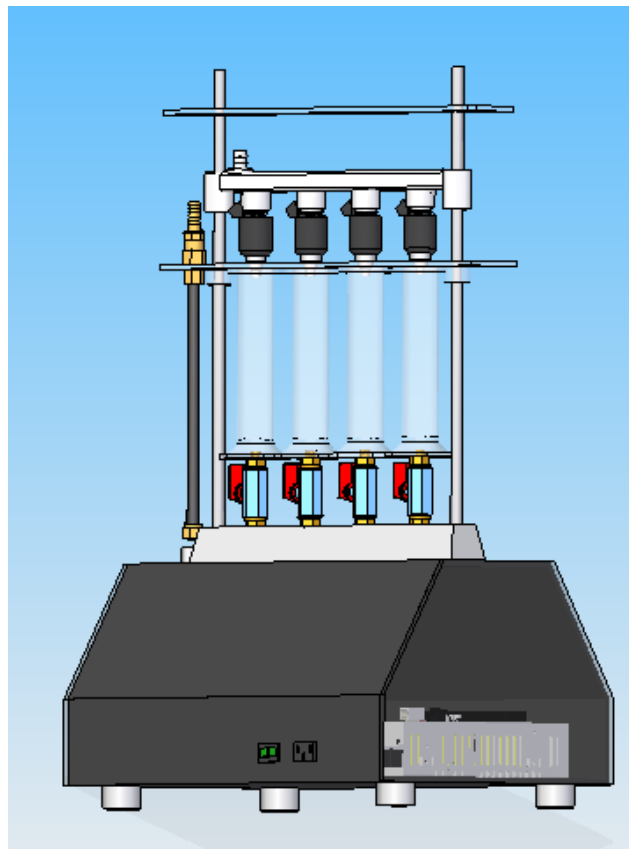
Diseño mecánico del banco de inyectores. Fuente: autor
